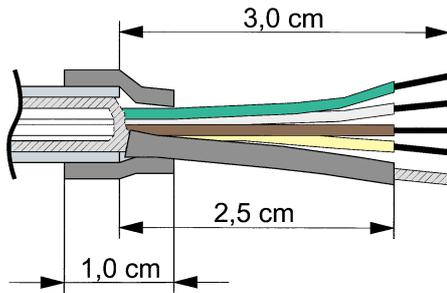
Bearbeitung des V24-Anschlußkabels des EPS 1001
